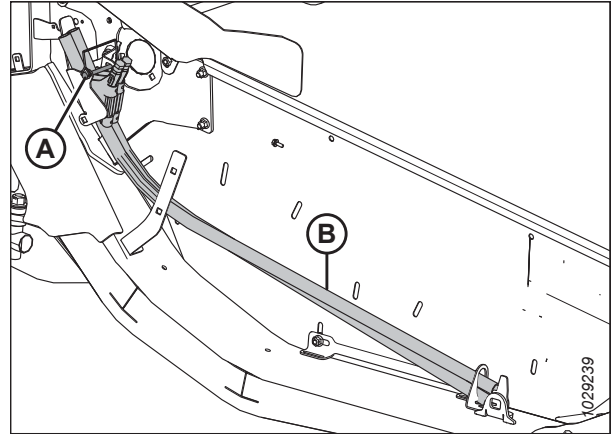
Skillestænger i opbevaringsplacering på skærebordets højre endeplade
